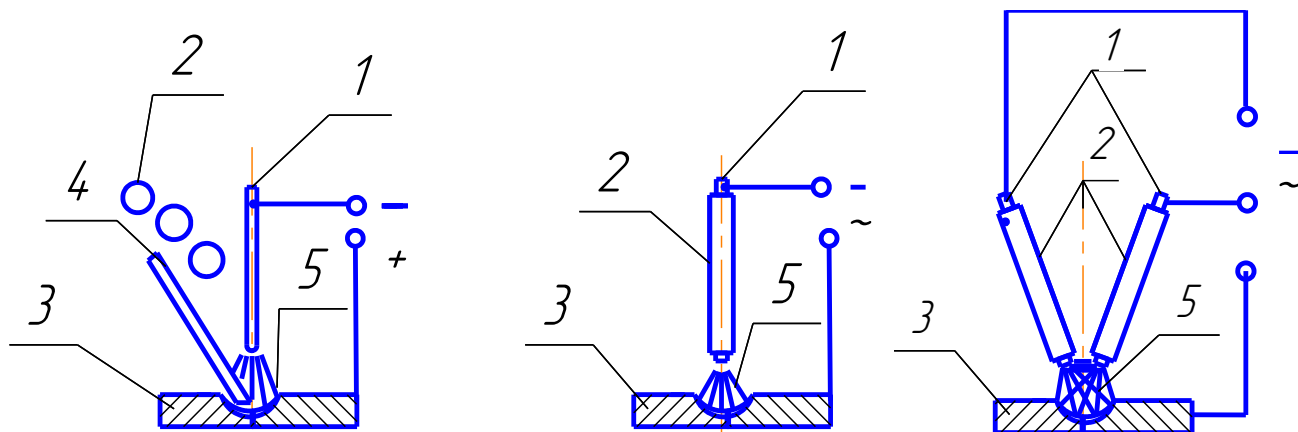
Принципиальные схемы основных способов ручной дуговой сварки:
